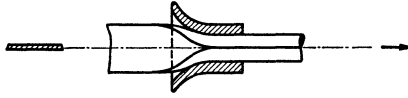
Stumpfschweißung durch Ziehen.
